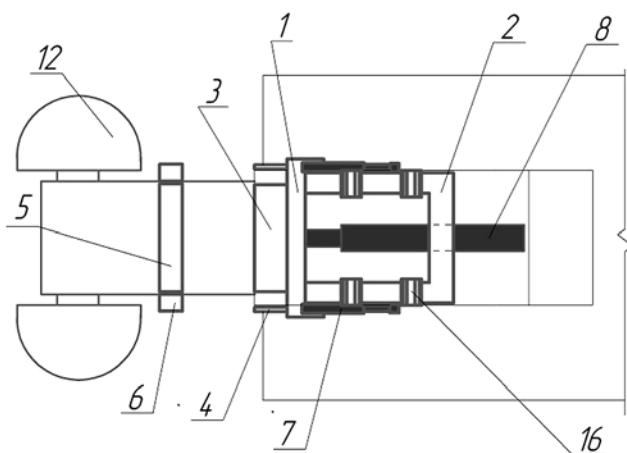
Исполнительный орган комбайна с крепеподъемником (вид сверху)
